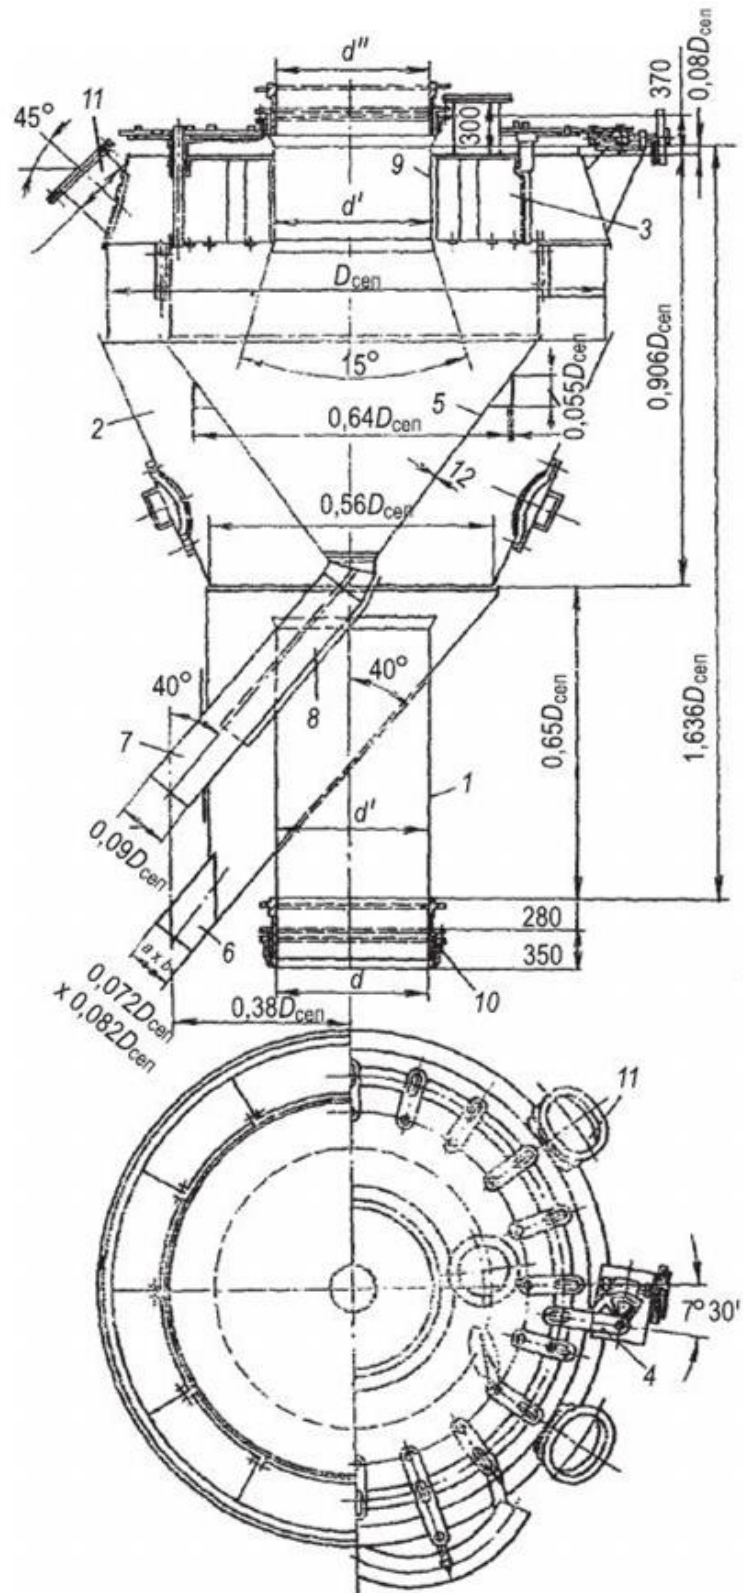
Відцентровий повітряно-прохідний сепаратор для ШБМ [15]: 1 - вхідний патрубок; 2 - зовнішній конус; 3 - регулювальні лопатки; 4 - привід лопаток; 5 - внутрішній конус; 6 - нижня труба повернення; 7 верхня труба повернення; 8 - броньова плита; 9 вихідний патрубок; 10 - сальниковий компенсатор; 11 - вибуховий клапан
